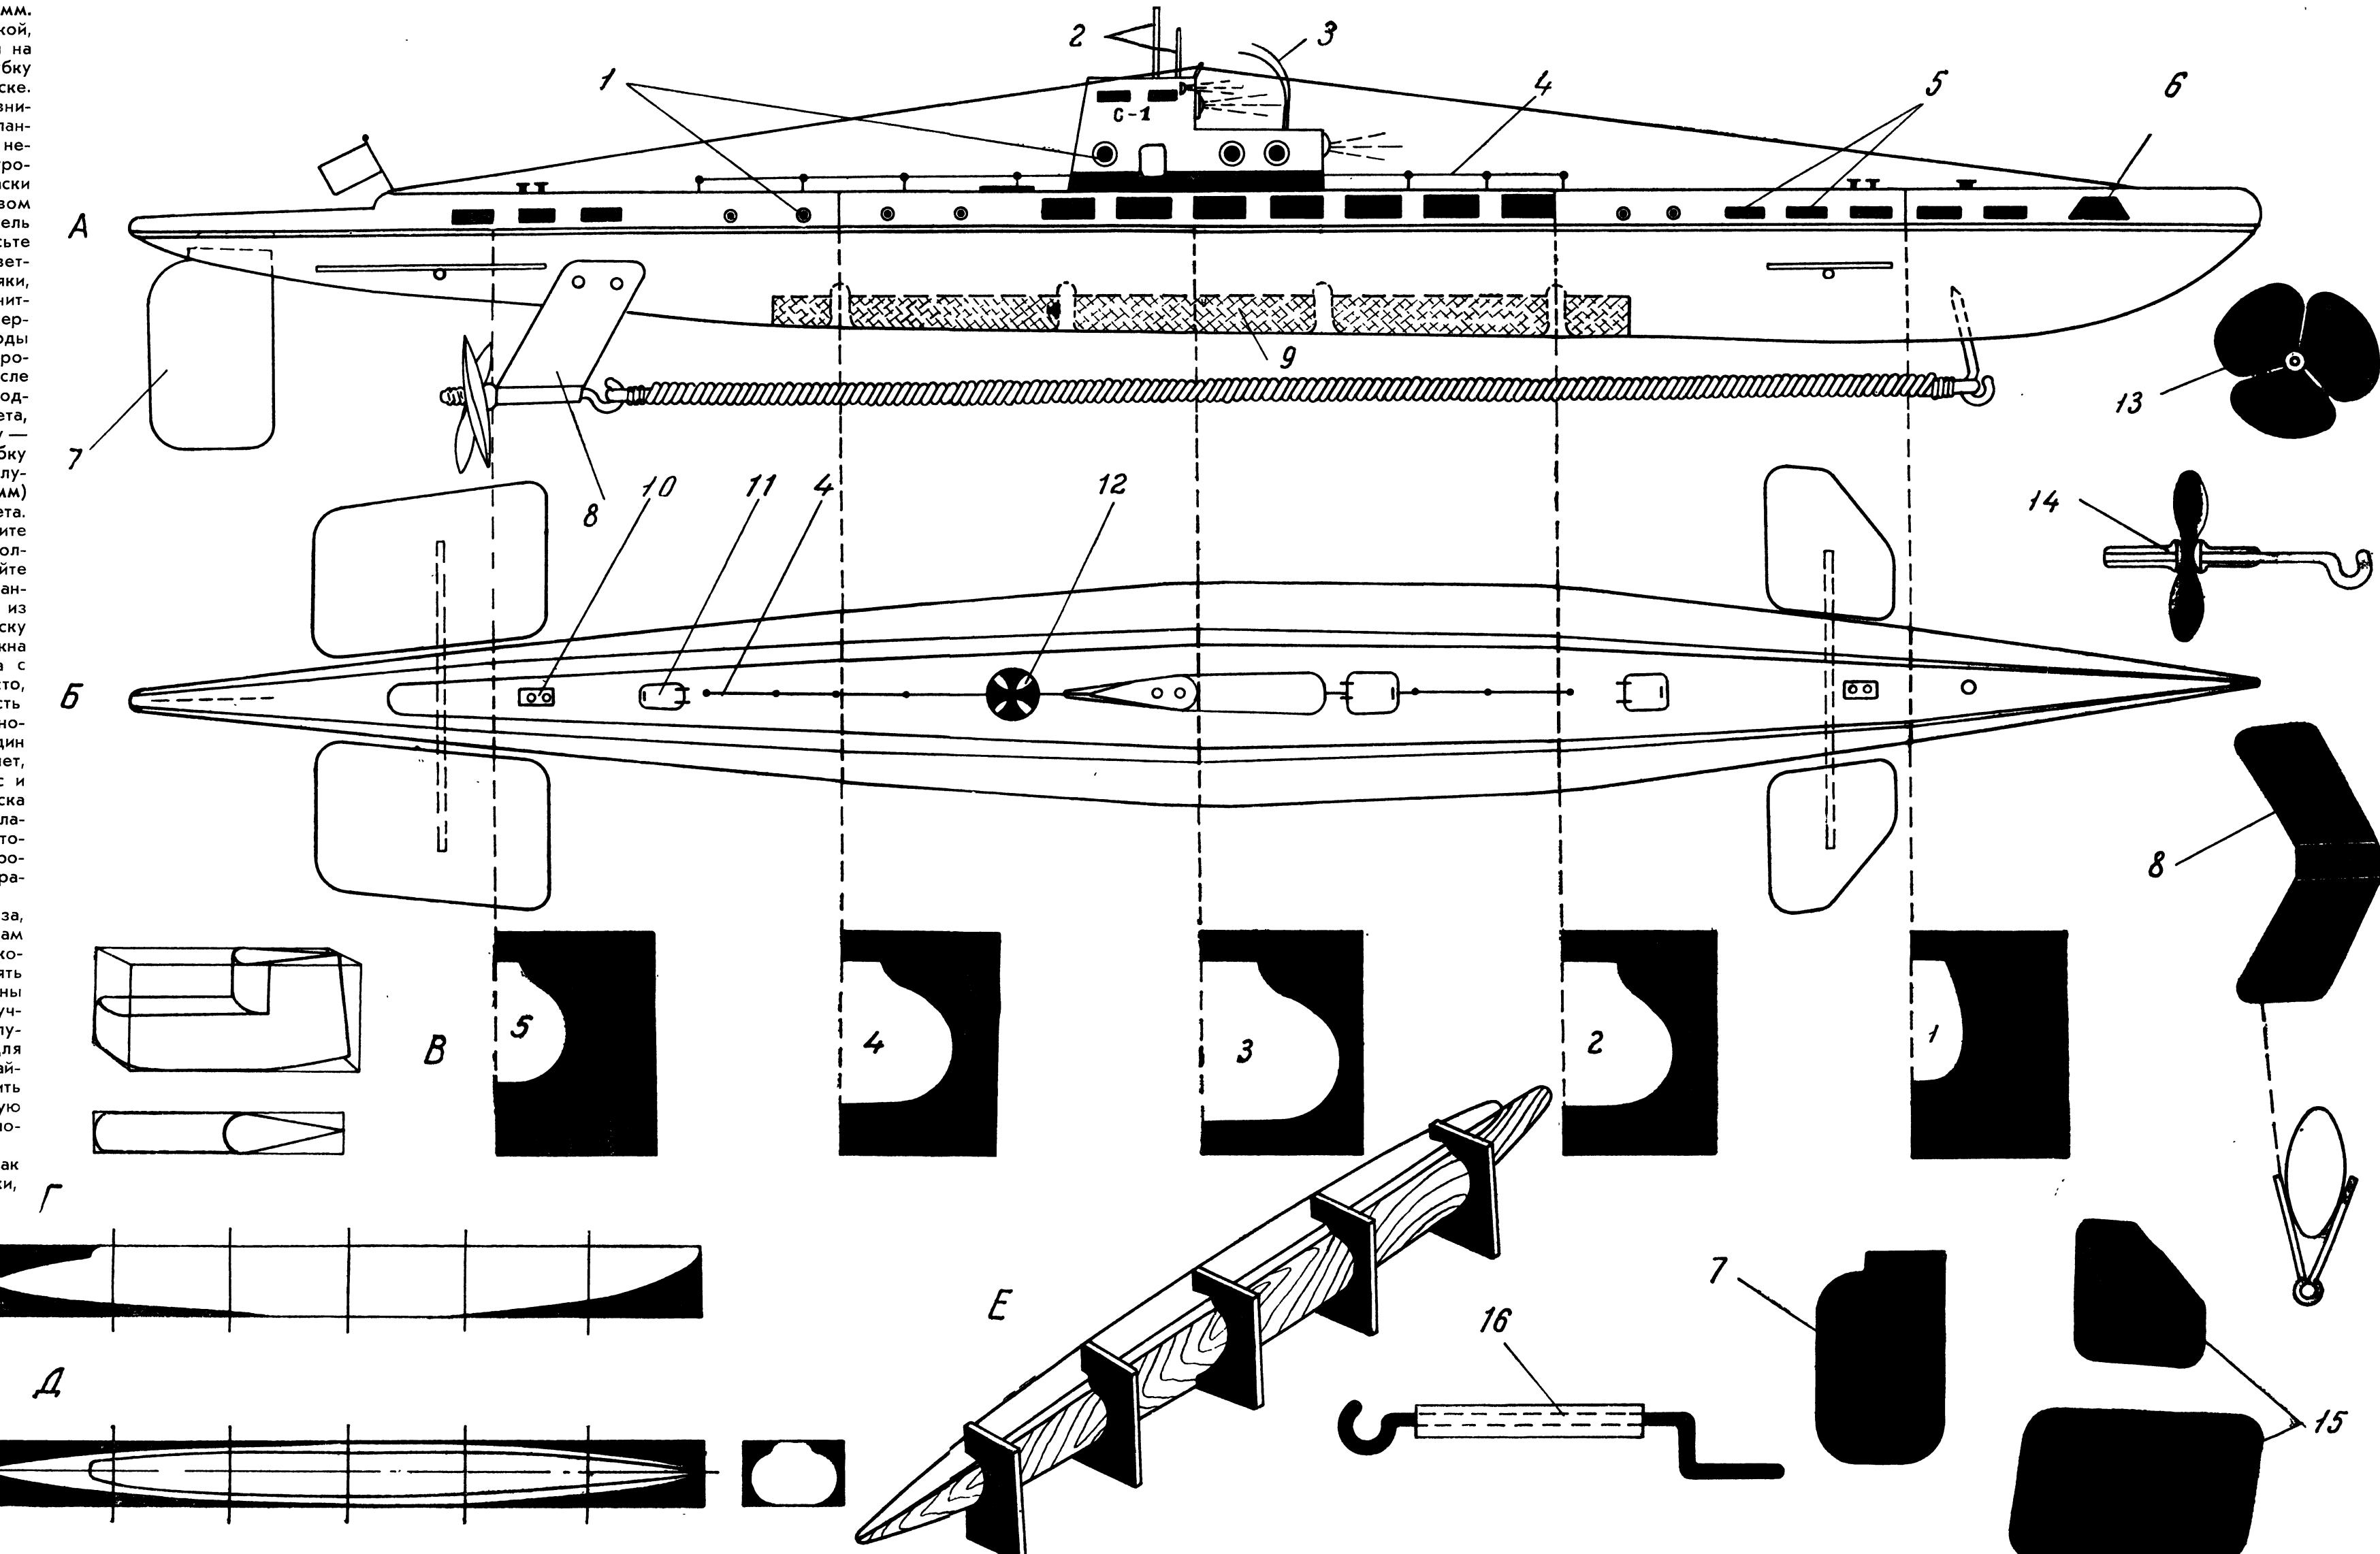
Модель подводной лодки „Севрюка“: А — вид сбоку; Б — вид сверху; В — шаблоны; Г — обработка рубки; Д — обработка корпуса и палубы лодки; Е — проверка шаблонами корпуса модели подводной лодки при её обработке.
